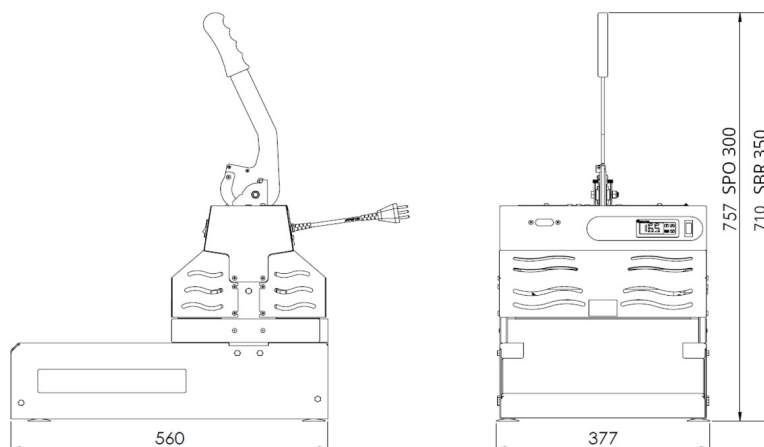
Dimensões gerais da máquina SPO 300 / SBR 300.
